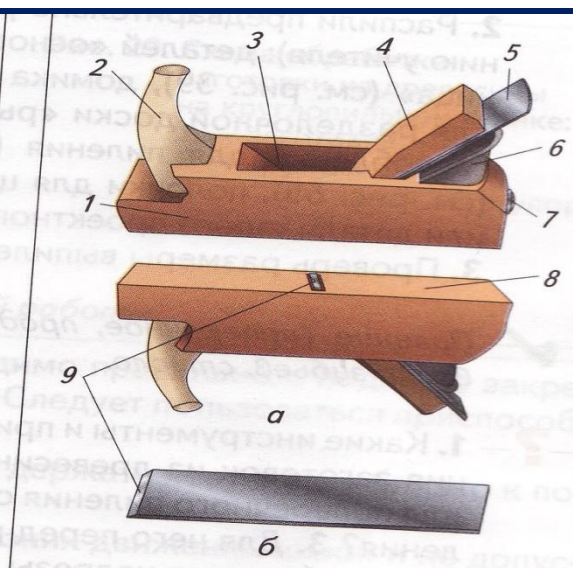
Рубанок: *а* — общий вид: 1 — колодка; 2 — рукоятка; 3 — леток; 4 — клин; 5 — нож; 6 — упор; 7 — пятка; 8 — подошва; 9 — лезвие; б — нож
